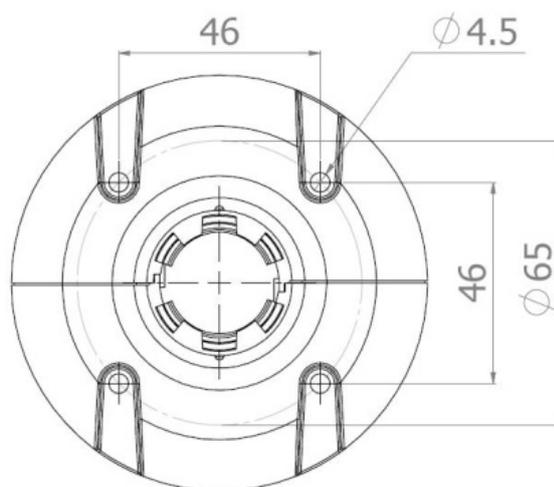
Размеры основания стойки и расположение отверстий для её крепления.
